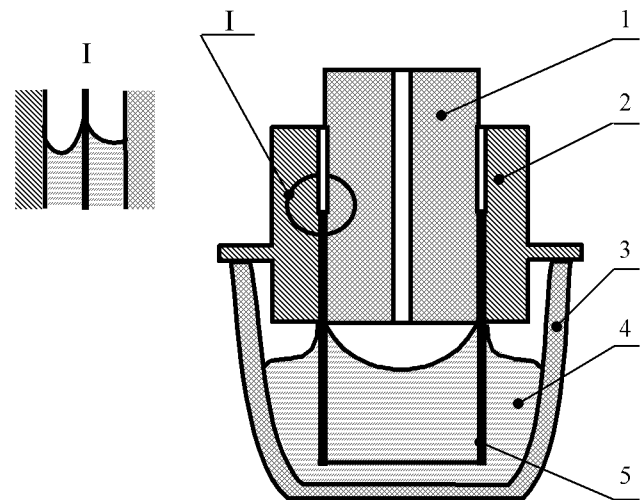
Схема сборочного узла керамика-металл для принудительной подачи припоя в паяный зазор: 1 — стекло или керамика, 2 — металлическая обойма, 3 — керамический вспомогательный тигель, 4 — припой, 5 — металлические проводники, по которым транспортируется припой
